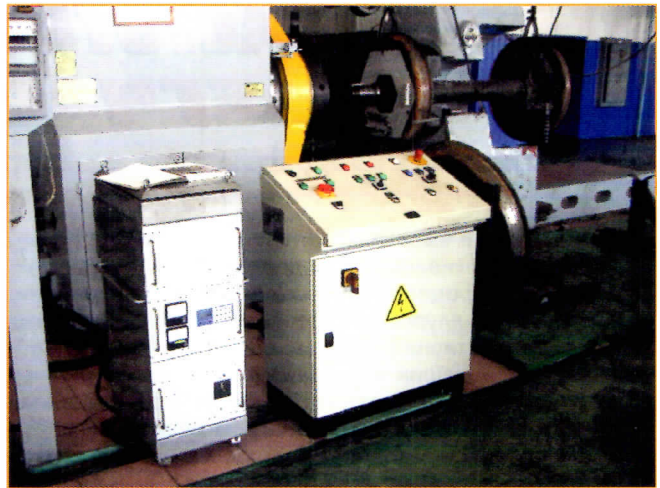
Установка индукционного нагрева УИН-006-50-T-001 совместно с прессом для распрессовки колесных пар
